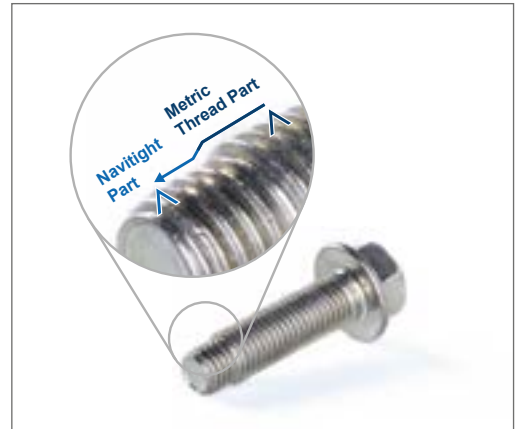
Montagegerechte Schraubenspitze Navitight®
